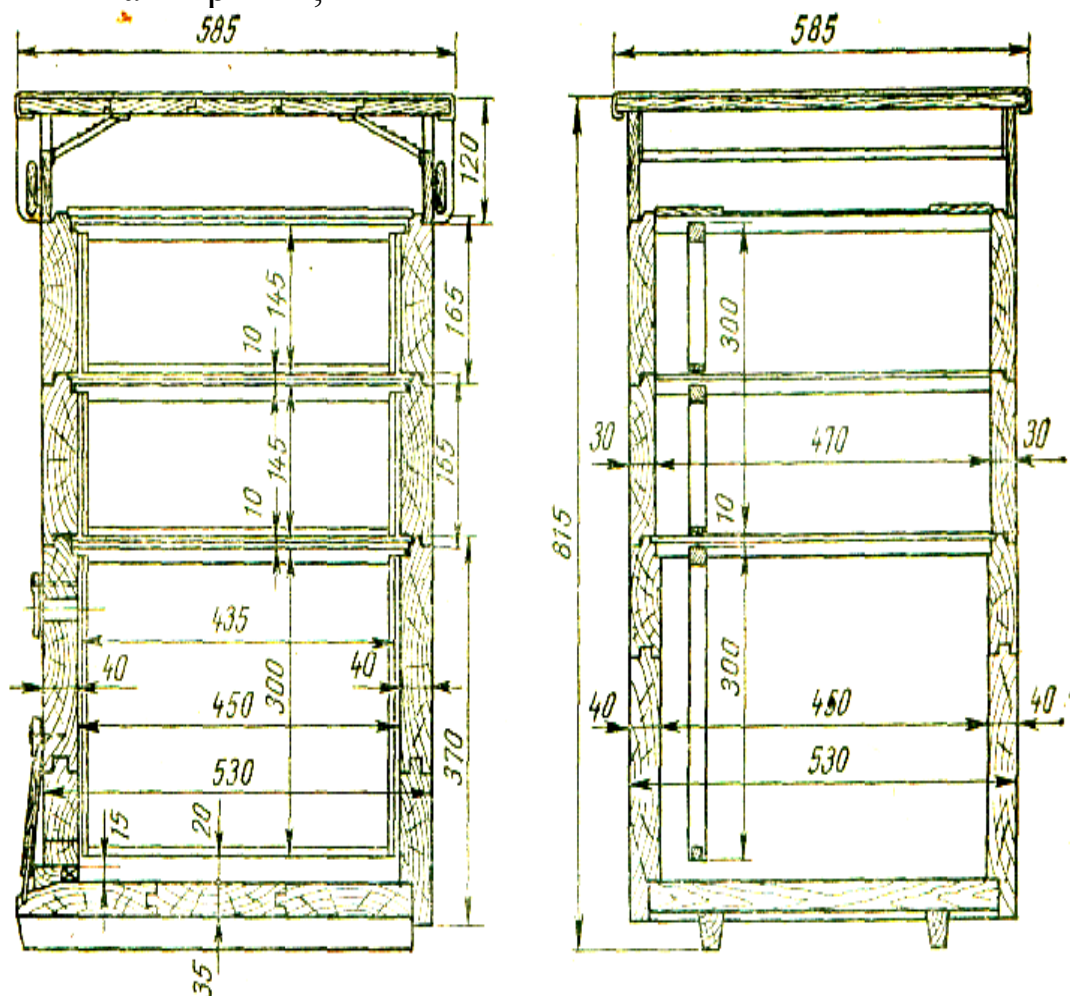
Схема однокорпусного (двенадцатирамочного) улья с двумя магазинными надставками: 1 - корпус; 2 - рамка гнездовая; 3 - диафрагма; 4 - магазин; 5 - рамка магазинная; 6 - подкрышник; 7 - крыша; 8 - задвижка верхнего летка; 9 - задвижка нижнего летка
